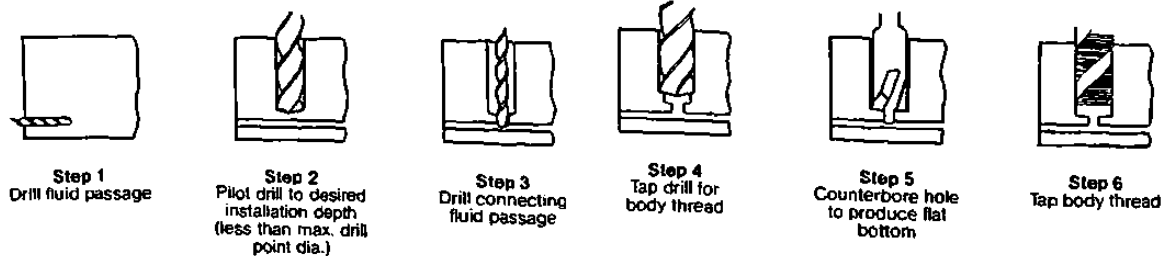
Secuencia de maquinados para instalar componentes en un sistema de montaje.
